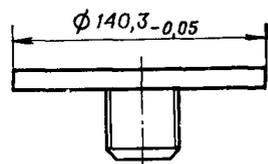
Калибр для проверки внутреннего диаметра трубы 8У36 С6 13-6
